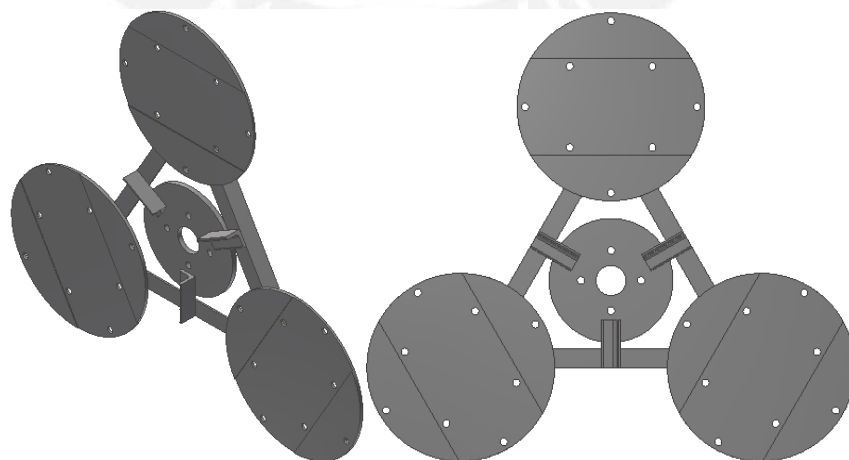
Vista isométrica (izquierda) y superior (derecha) del arreglo de moldes.
